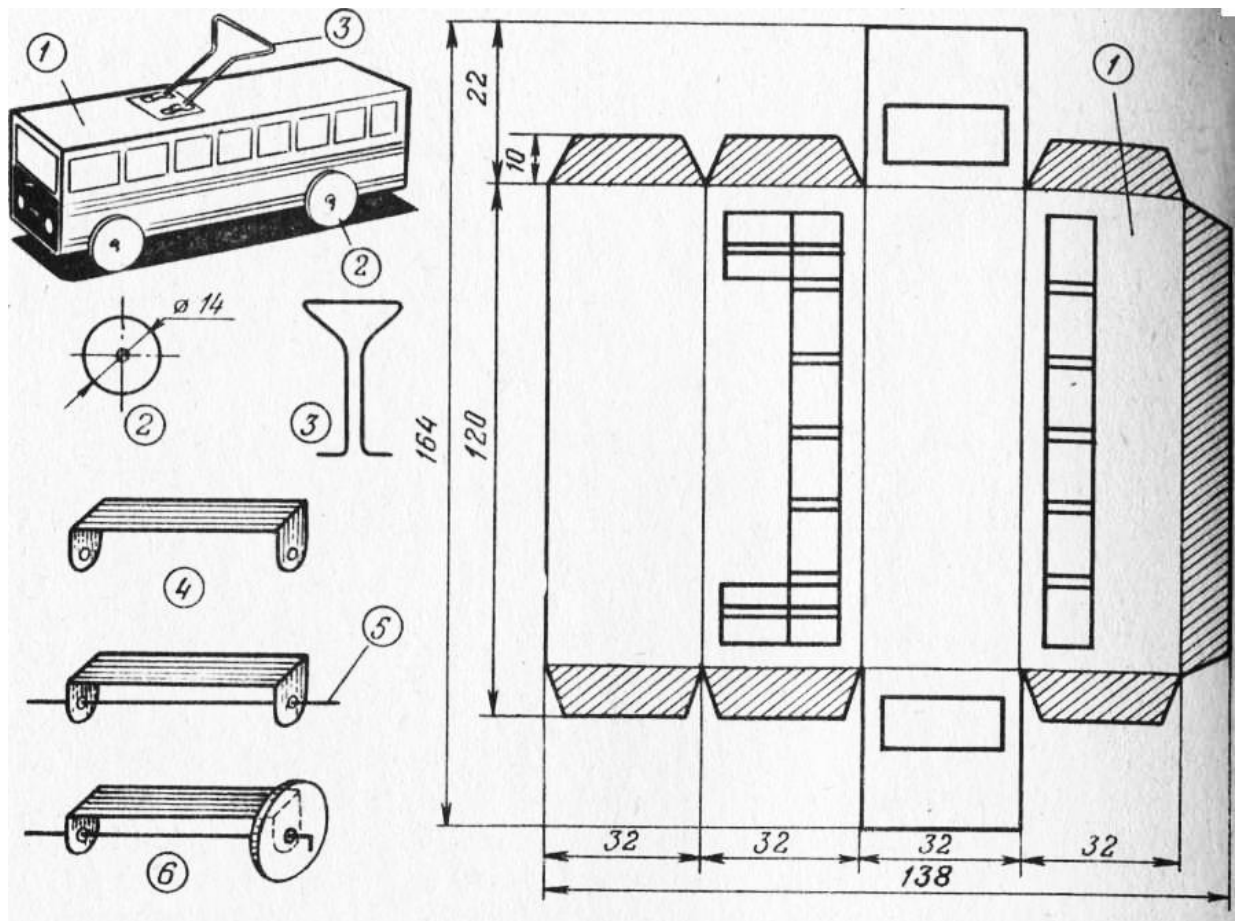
Модель трамвая: 1 — развертка кузова; 2 — колесо; 3 — дуга; 4—скоба; 5— ось; 6— сборка моста ходовой части
